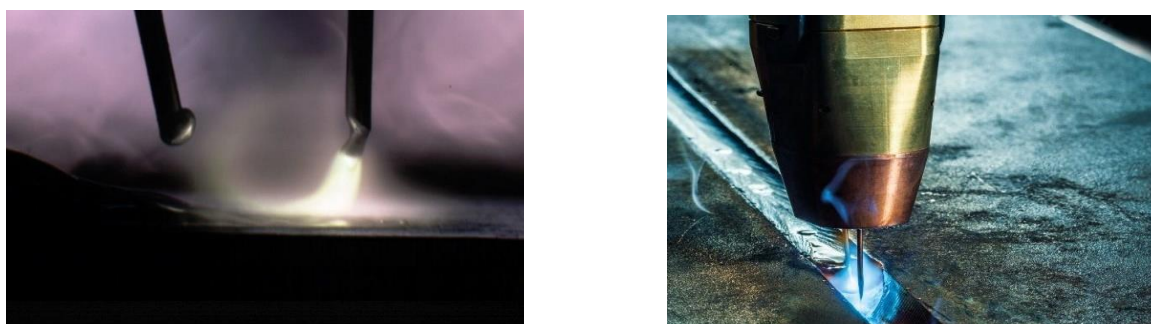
работа сварочной дуги в процессе СМТ Twin
